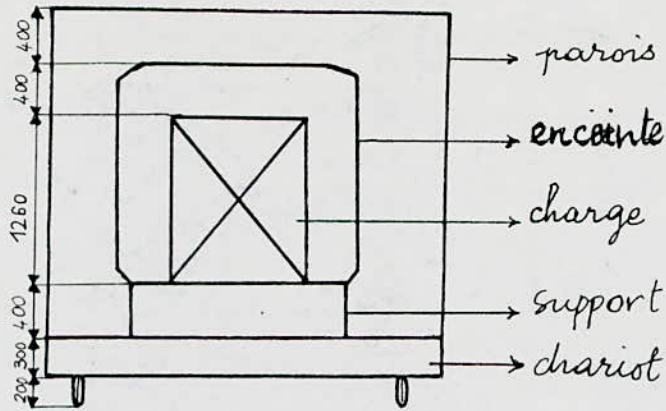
Coupe transversale du Four (Dimension selon la hauteur)
